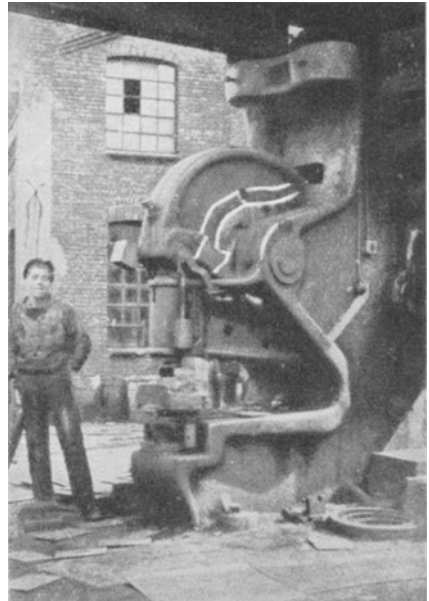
Schweißung des Balancers einer Schiffbaustanze.
